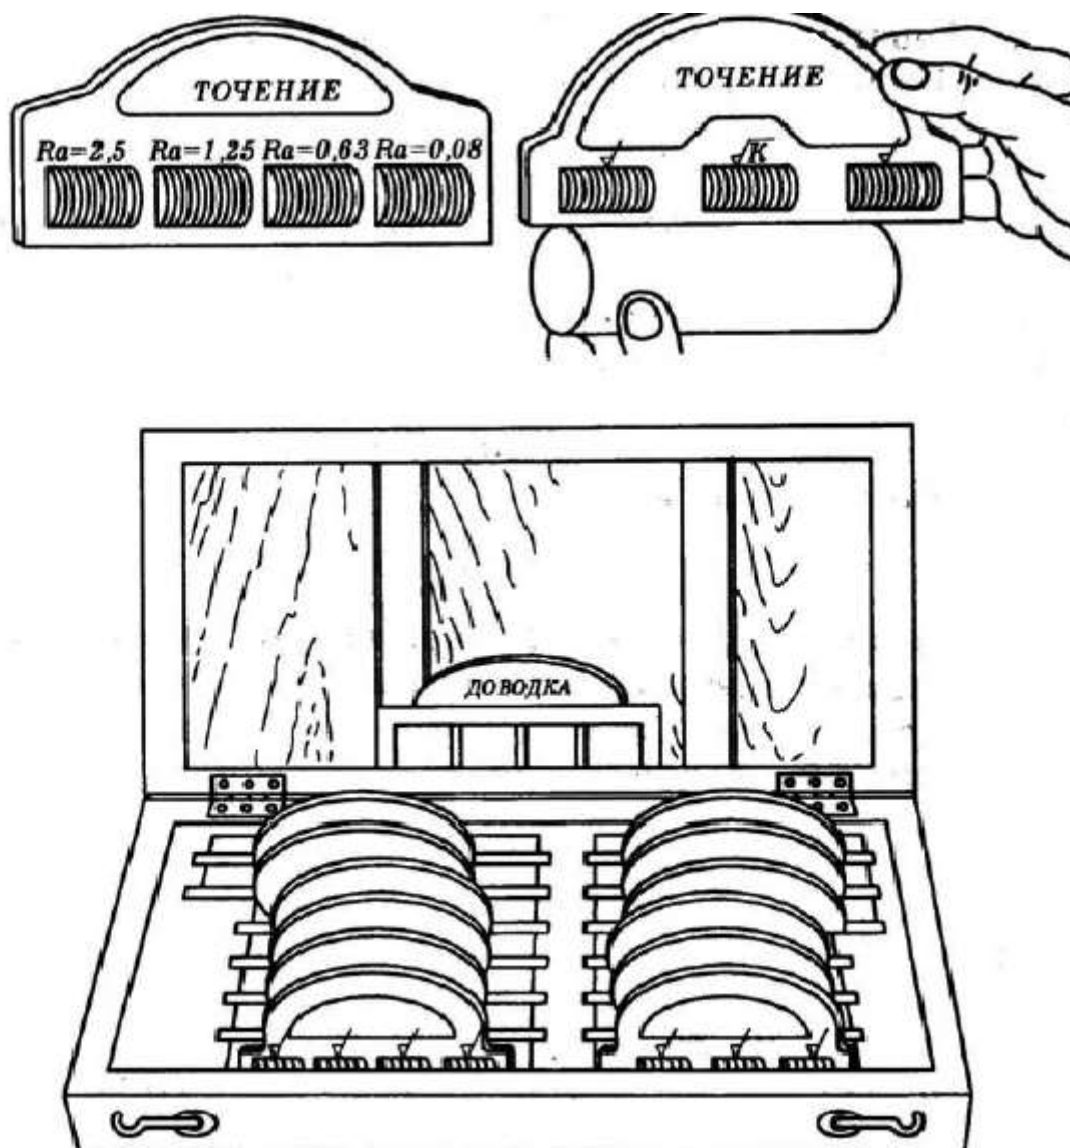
Комплект рабочих эталонов для контроля шероховатости поверхности
